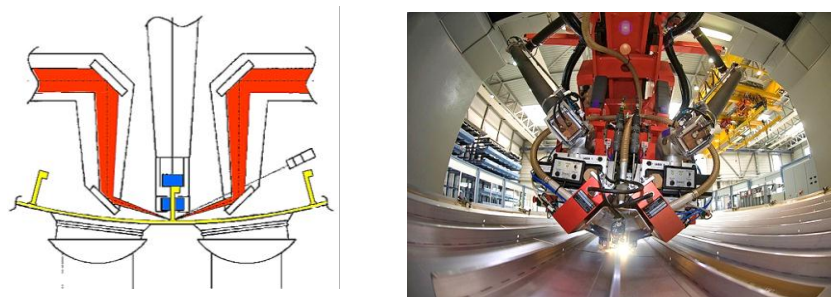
Технологическая схема и процесс лазерной сварки панелей фюзеляжа
